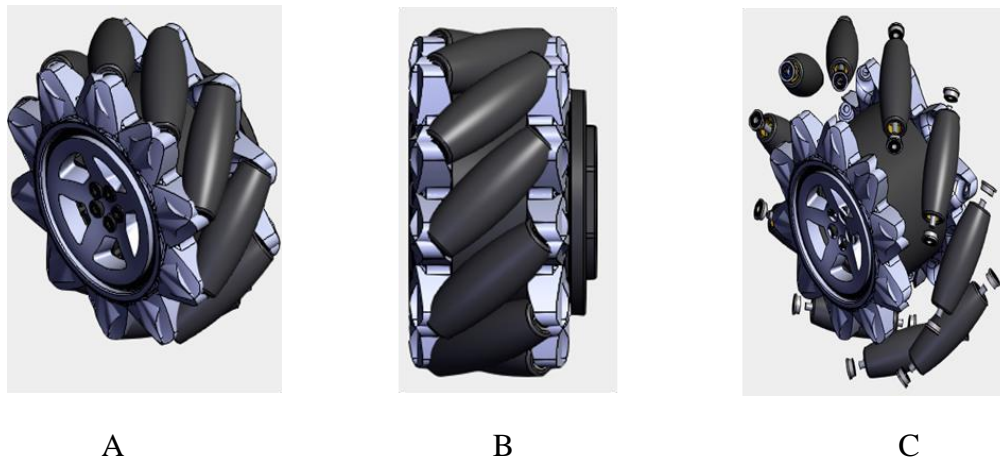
(A) Vue isométrique et (B) vue de face (C) vue éclaté de la roue mécanique
